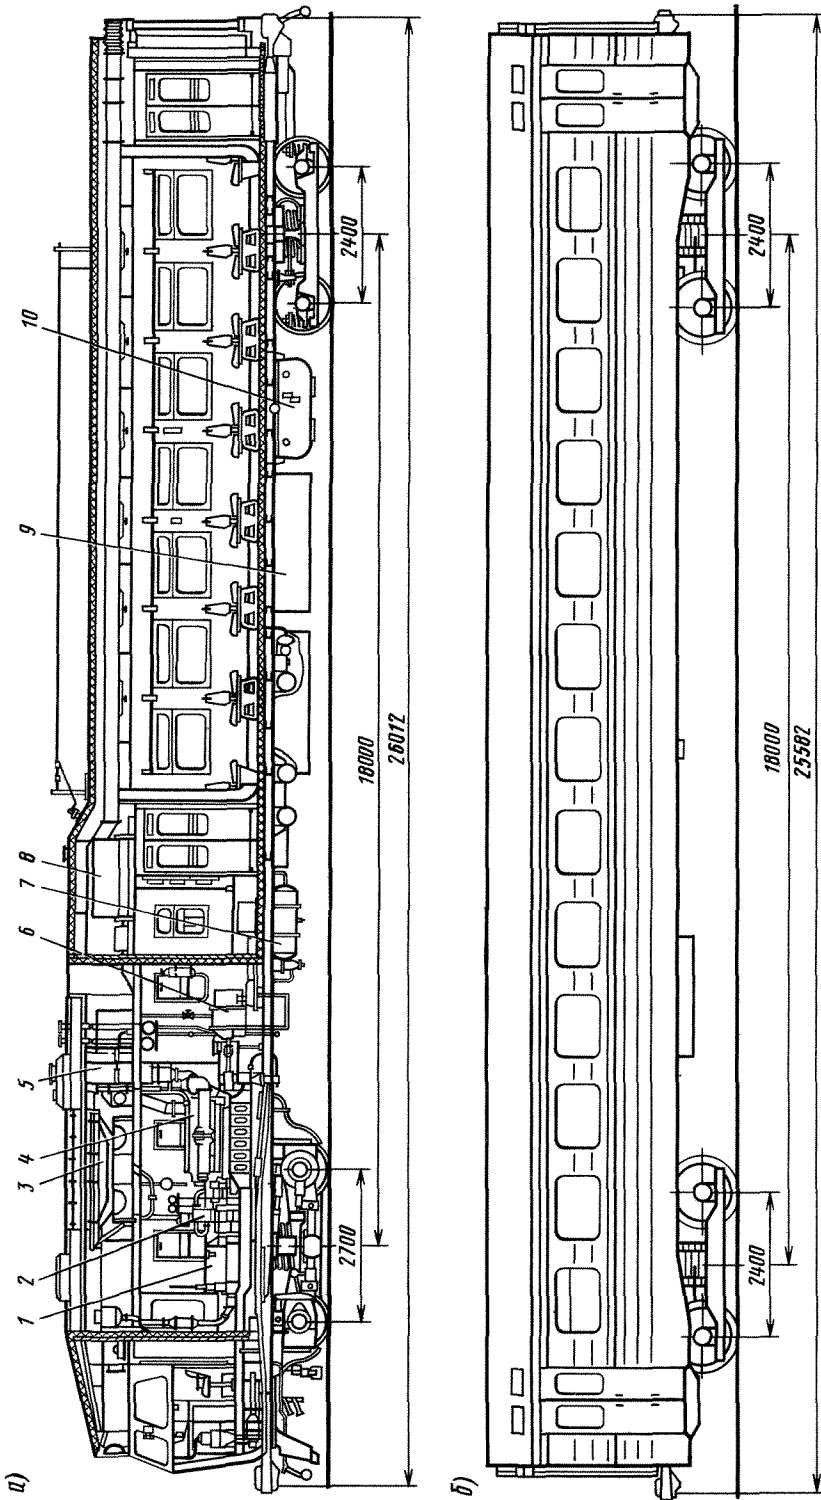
Расположение оборудования и основные размеры моторного (а) и прицепного (б) вагонов дизель поезда ДР1А
